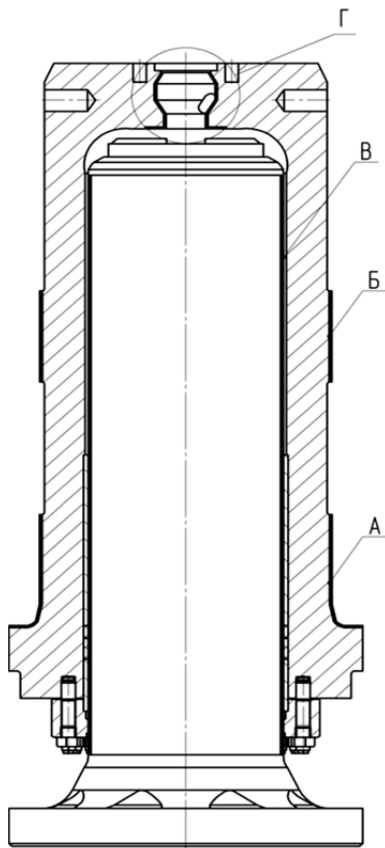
Загальний вигляд корпусу робочого циліндра гідравлічного преса з елементами та поверхнями зношення
